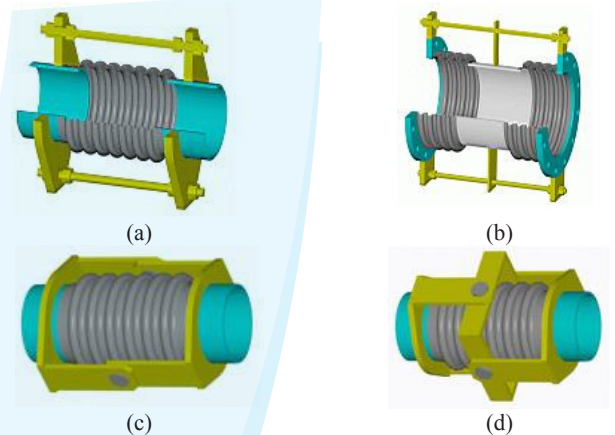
Tipos de Junta de Expansão. (a) Junta Atirantada Simples, (b) Junta Universal Atirantada, (c) Junta Rotulada Simples ou dobradiça, (d) Junta Bi-Rotulada ou Cardânica
